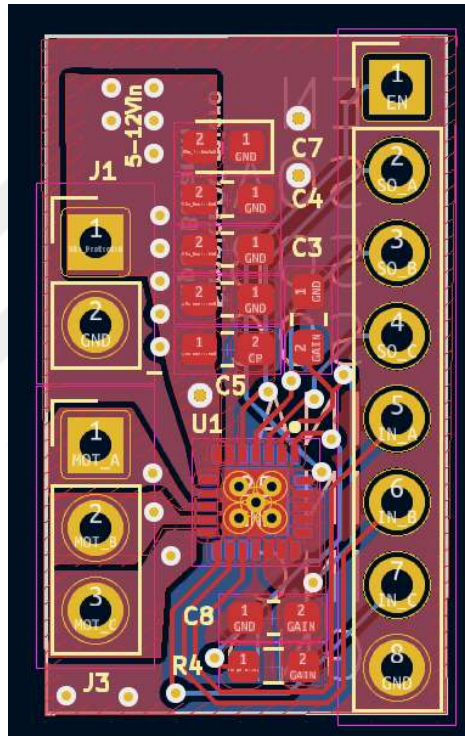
Motor Sürücü Entegresi Şematik Tasarımı
